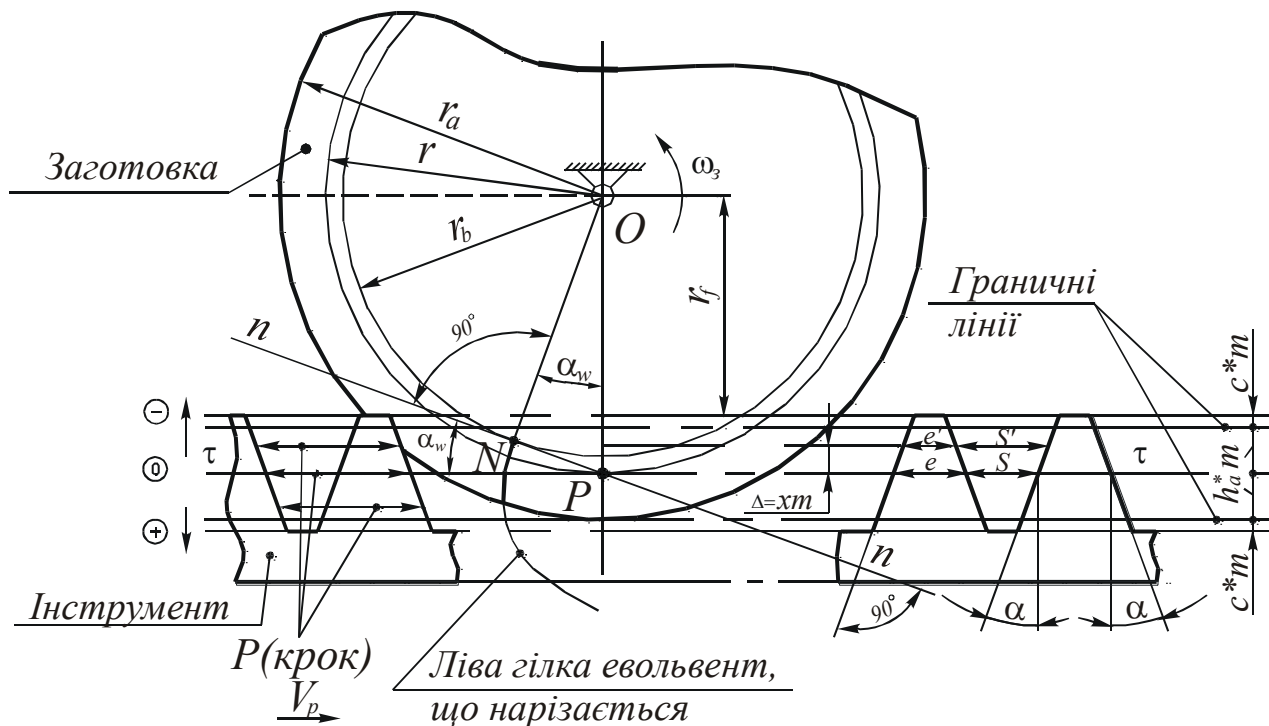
Верстатне зачеплення евольвентного колеса, що нарізається з рейковим інструментом
